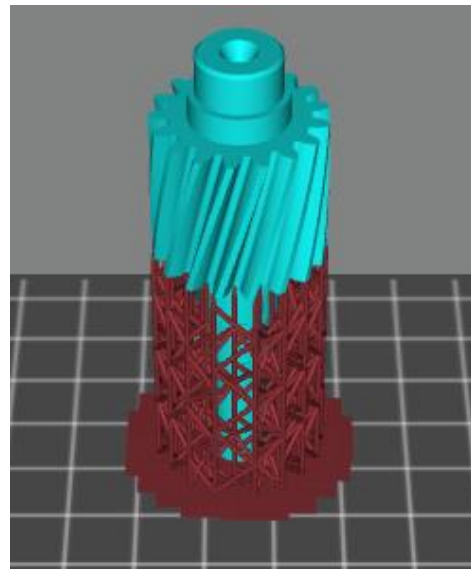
Опорні конструкції для 3D друку зубчастих коліс
